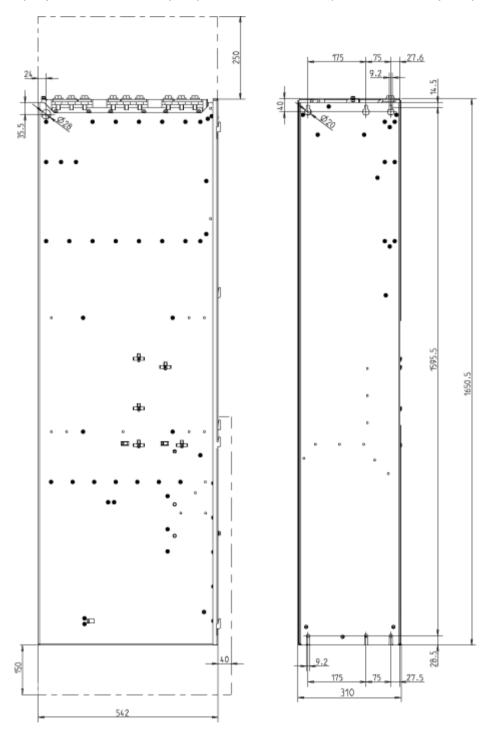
Чертеж общего вида модуля питания Basic, типоразмер GB, GD. Вид сбоку, вид сзади
